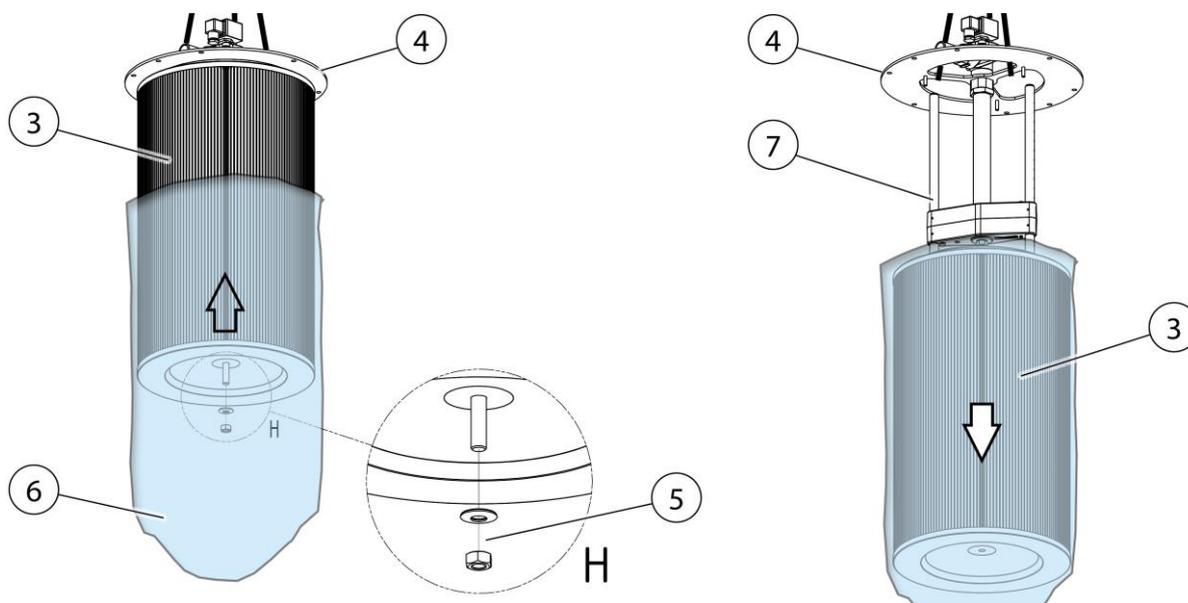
Remplacement du filtre – Démontage de la cartouche filtrante
